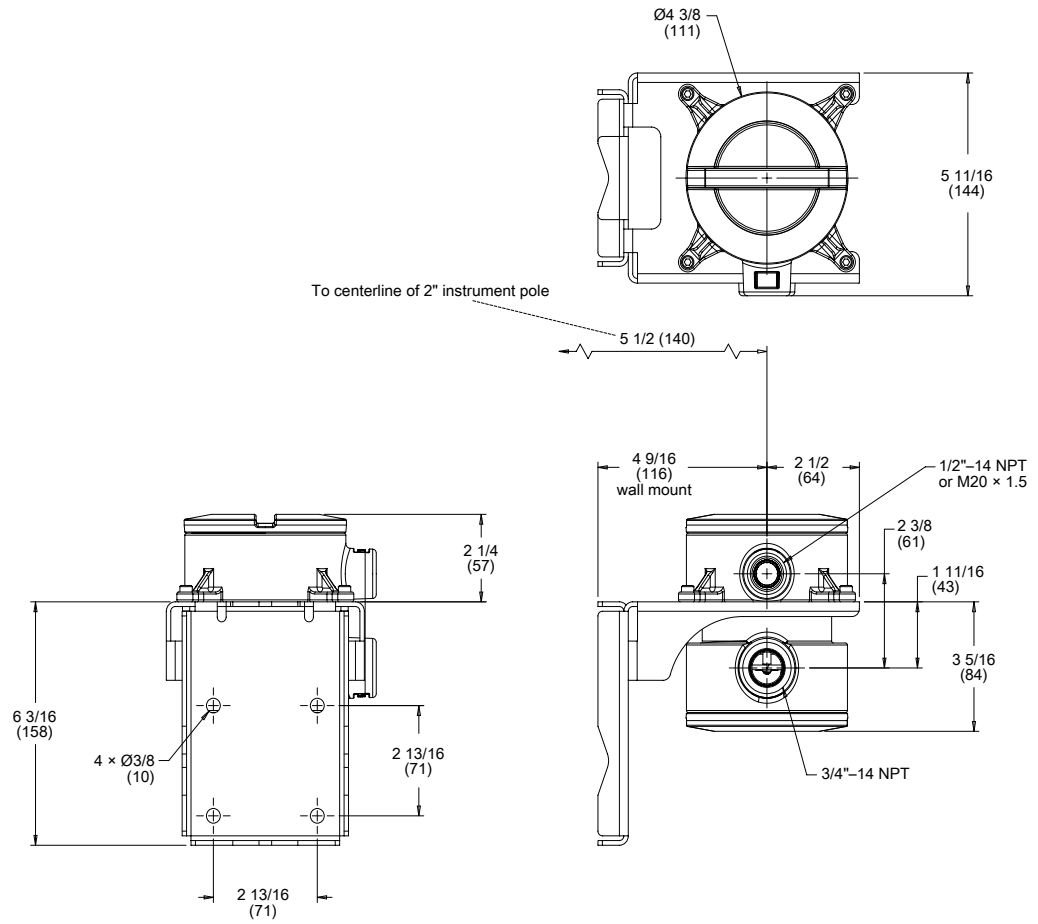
Dimensions de la platine processeur avancée déportée
